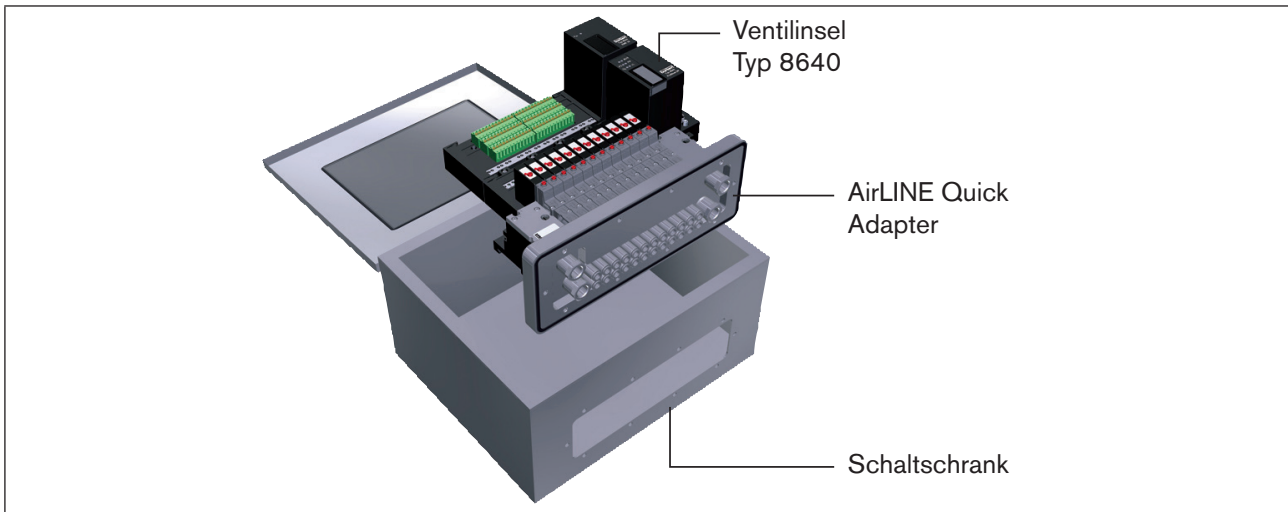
Platzieren der Ventilinsel im Schaltschrank
